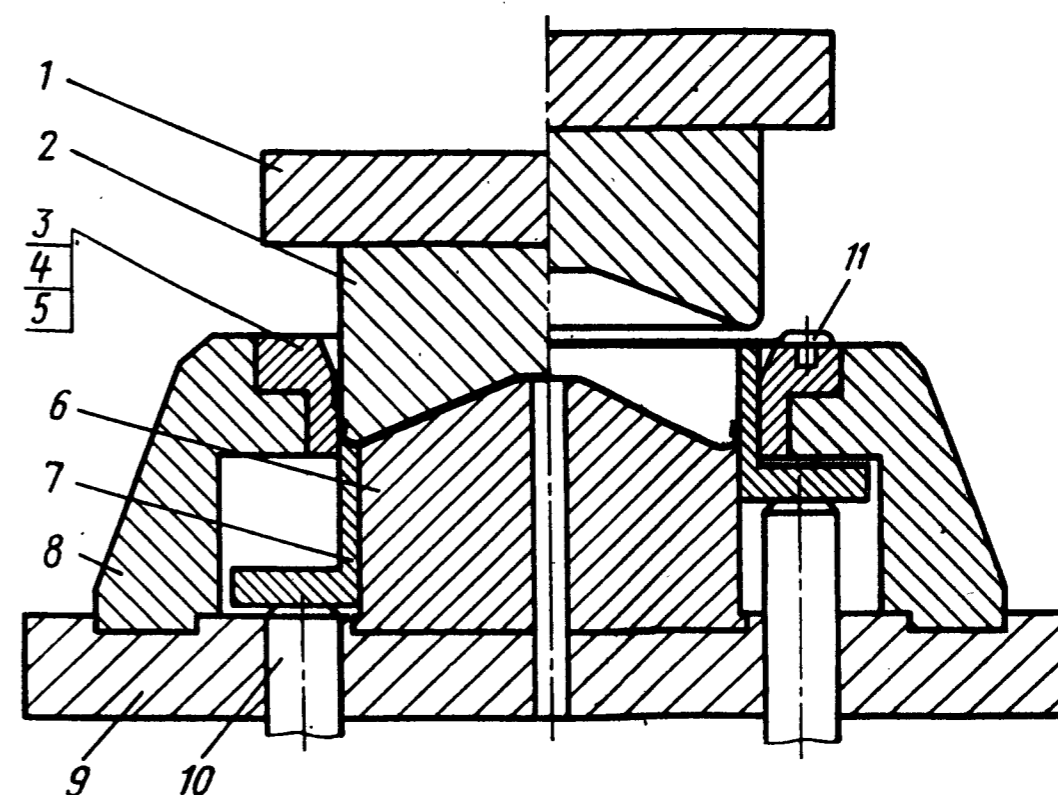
Штамп для однооперационной реверсивной вытяжки конической детали с фигурным фланцем
